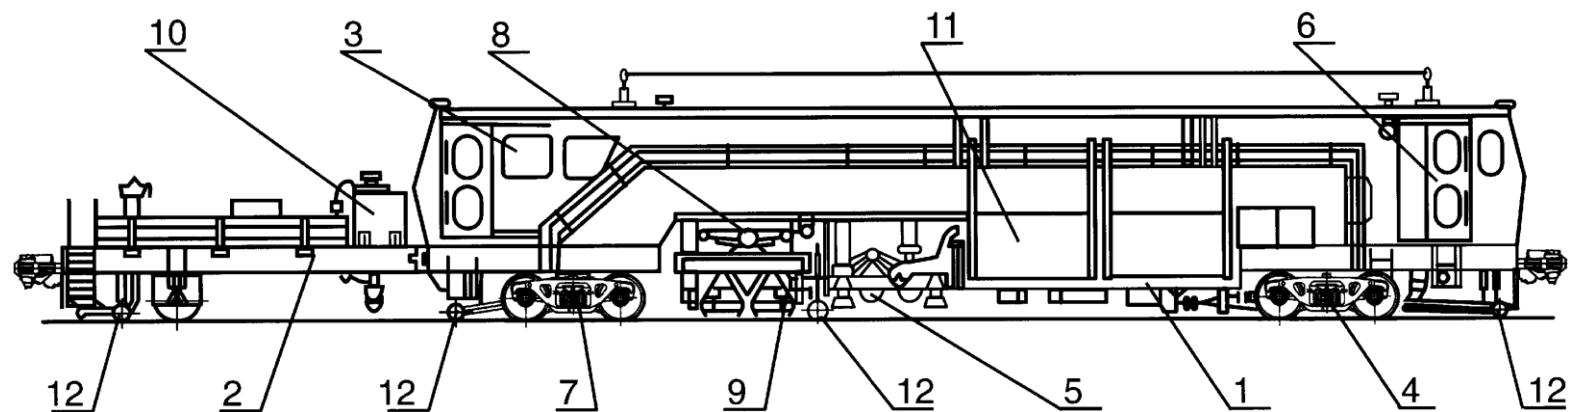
Выправочно-подбивочно-рихтовочная машина ВПР-02: 1 – рама; 2 – платформа полуприцепная; 3, 6 – кабина; 4, 7 – тяговая и бегунковая тележки; 5 – подъёмно-рихтовочное устройство; 8 – подбивочный блок; 9 – уплотнитель балласта; 10 – топливный бак; 11 – силовая установка; 12 – контрольно-измерительные тележки
